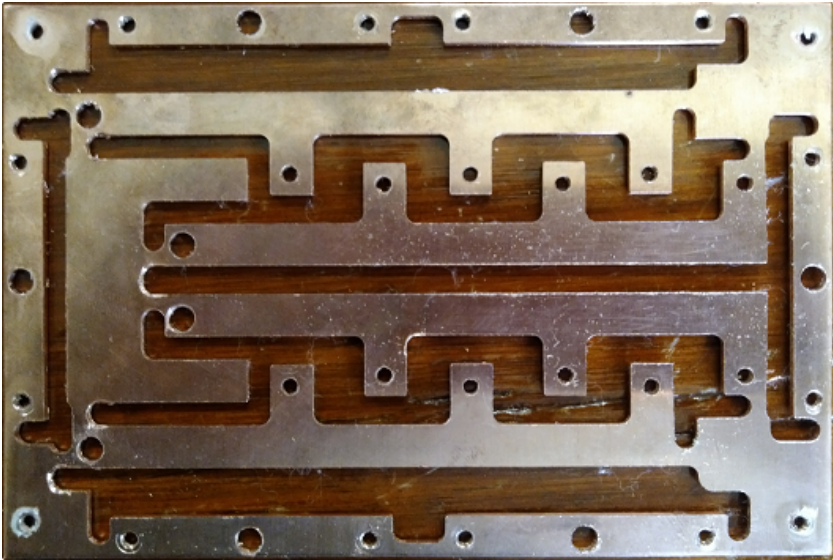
Placa de cobre maquinado en CNC para refuerzo de pistas
